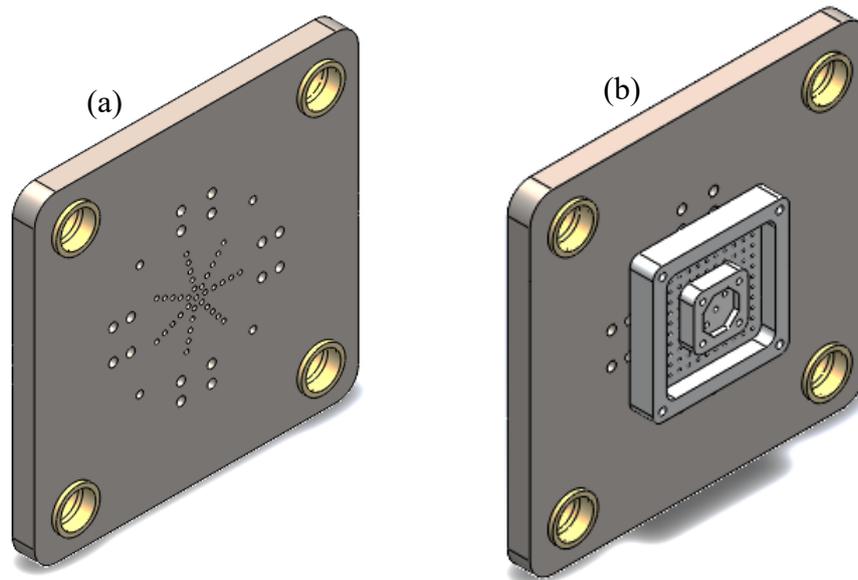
Placa móvel: (a) sem o porta molde e (b) com o porta molde
